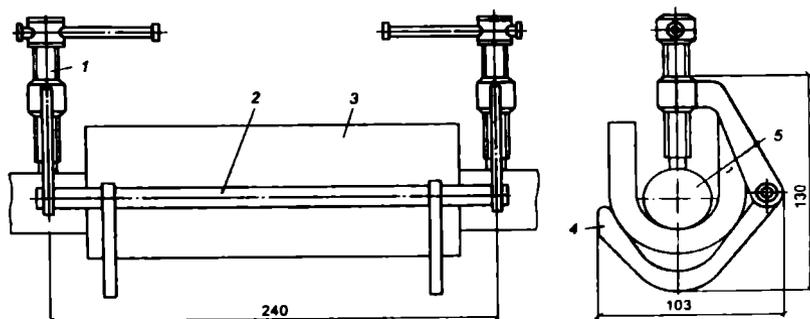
Приспособление для закрепления желобчатых подкладок:
